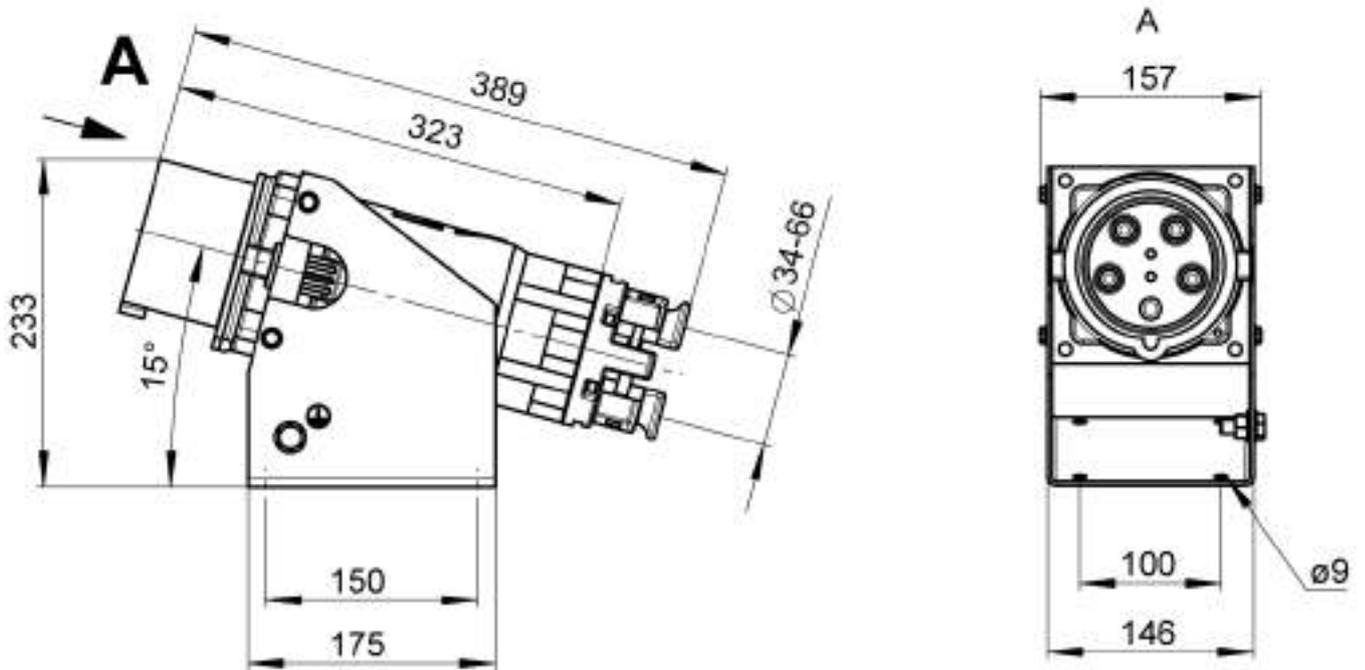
Abmessungen Gerätestecker MCW D-Line, C-Line (160A – 250 A) in mm
